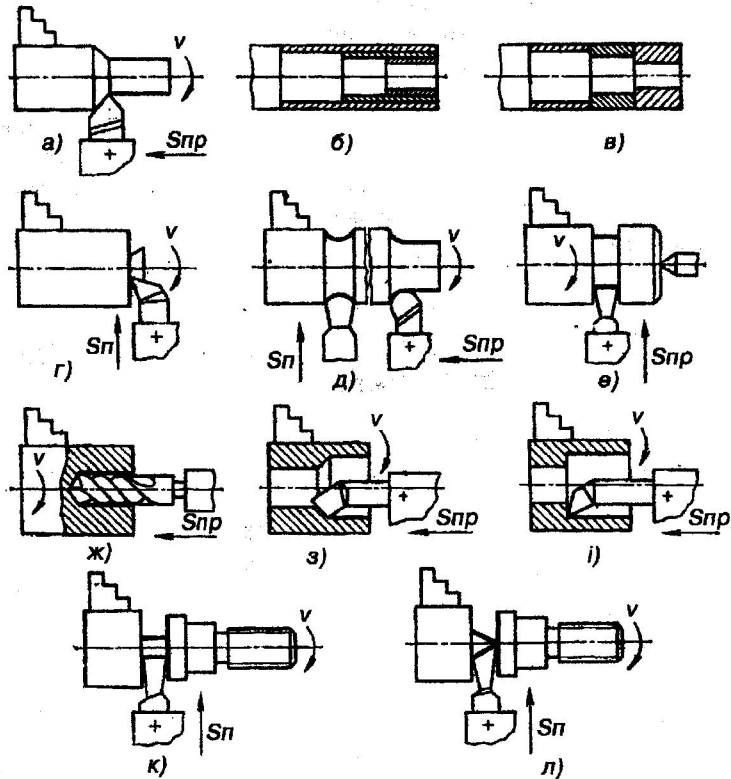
Схеми обробки заготовок на токарно-гвинторізному верстаті
